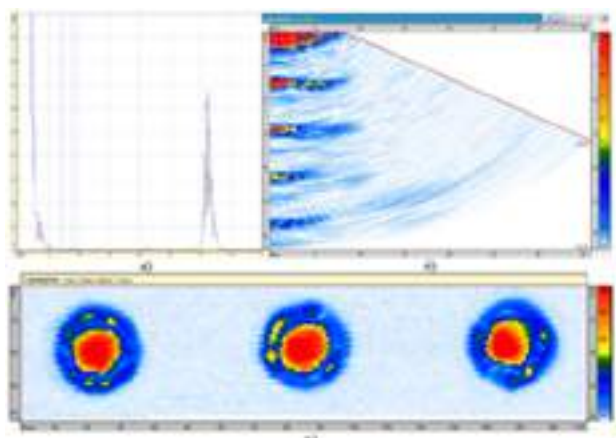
Тестовые измерения сварных швов с помощью ультразвукового неразрушающего контроля.
